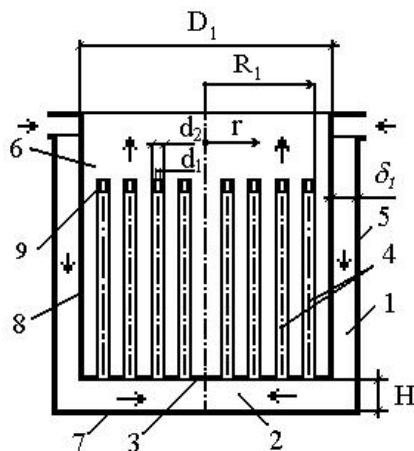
Конструкция цилиндрической РКС с боковым подводом потока через боковой кольцевой канал: 1 – боковой канал; 2 – коллектор; 3 – трубная доска; 4 – трубный пучок; 5 – корпус; 6 – выходная камера; 7 – днище; 8 – внутренняя обечайка; 9 – диафрагма
